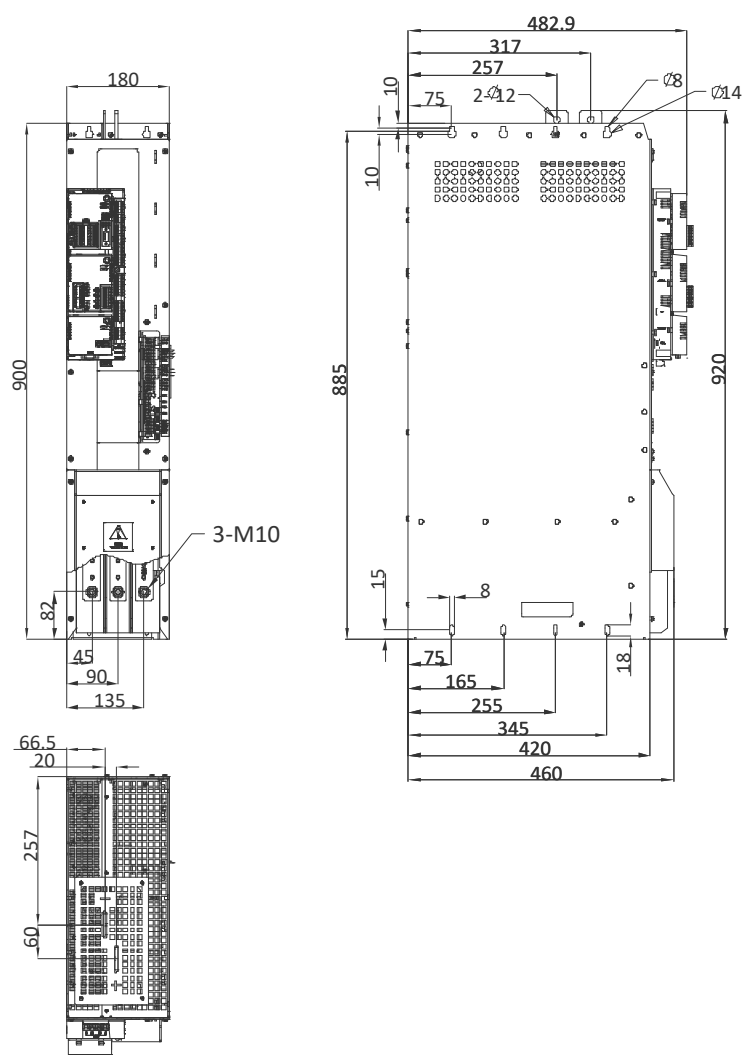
Габаритные размеры инвертора корпуса FR7 (мм)
